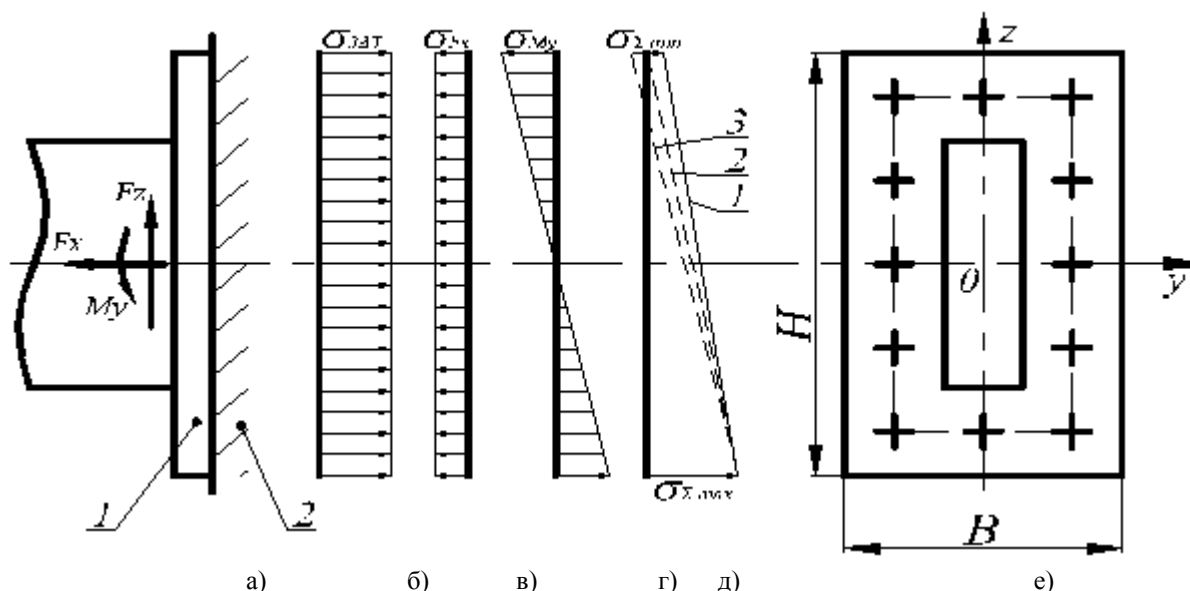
Схема к расчету силы затяжки фундаментных болтов:
